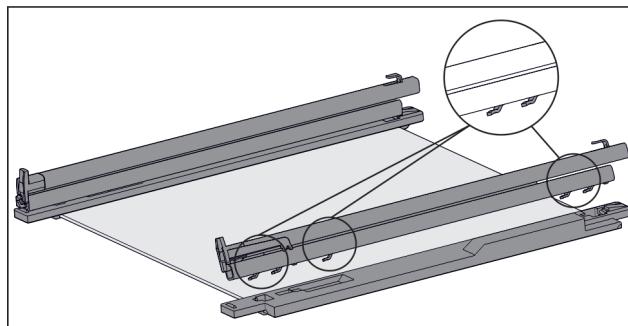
Скляна пластина з рейками та деталями для підтримки
